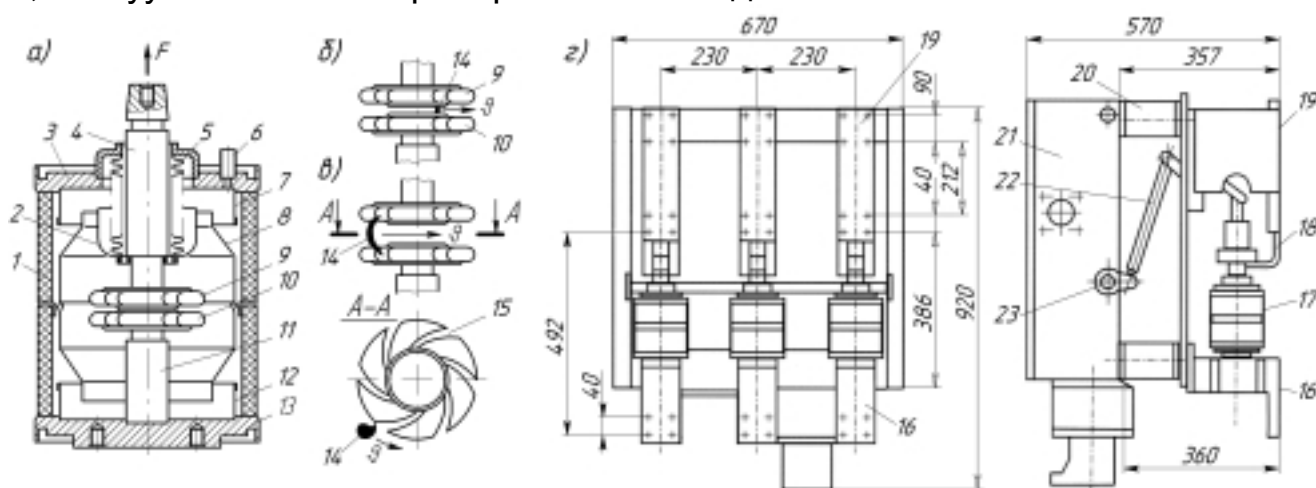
Вакуумный выключатель типа ВВРТ-10: конструкция вакуумной камеры (разрез) (а), метод гашения дуги между контактами камеры (б, в) и габаритные размеры выключателя (г)
